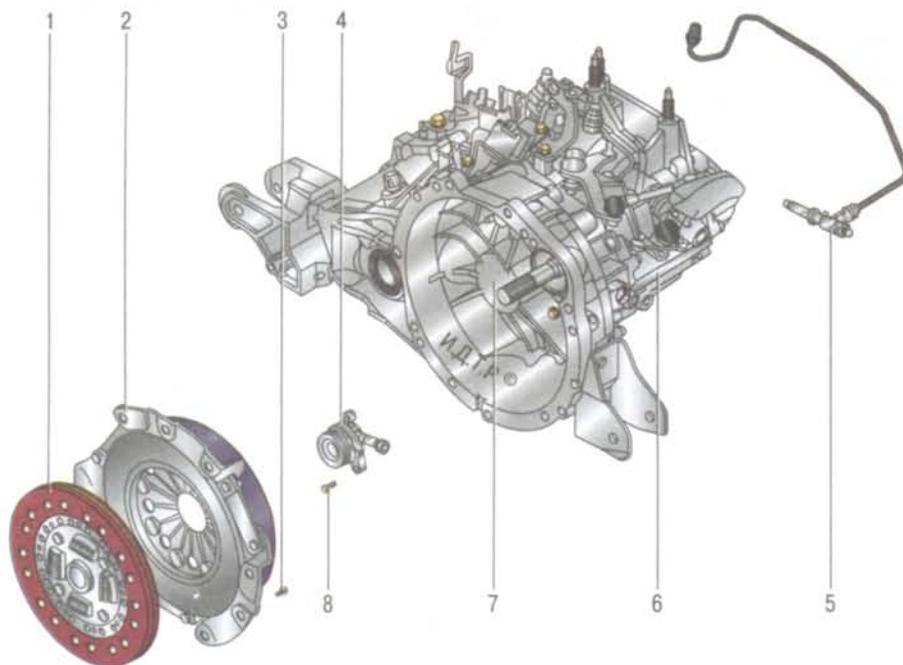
Сцепление: 1 – ведомый диск; 2 – кожух сцепления с нажимным диском; 3 – болт крепления кожуха сцепления к маховику двигателя; 4 – подшипник и рабочий цилиндр выключения сцепления; 5 – штуцер гидропривода выключения сцепления; 6 – коробка передач; 7 – картер сцепления; 8 – болт крепления подшипника рабочего цилиндра с подшипником выключения сцепления
